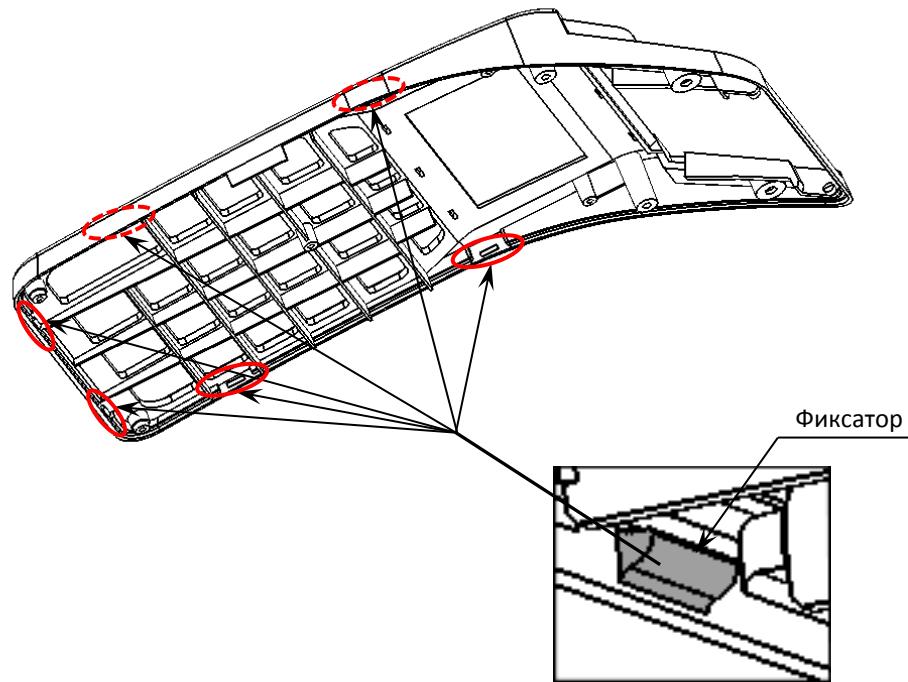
Расположение фиксаторов в верхней части корпуса ККТ
